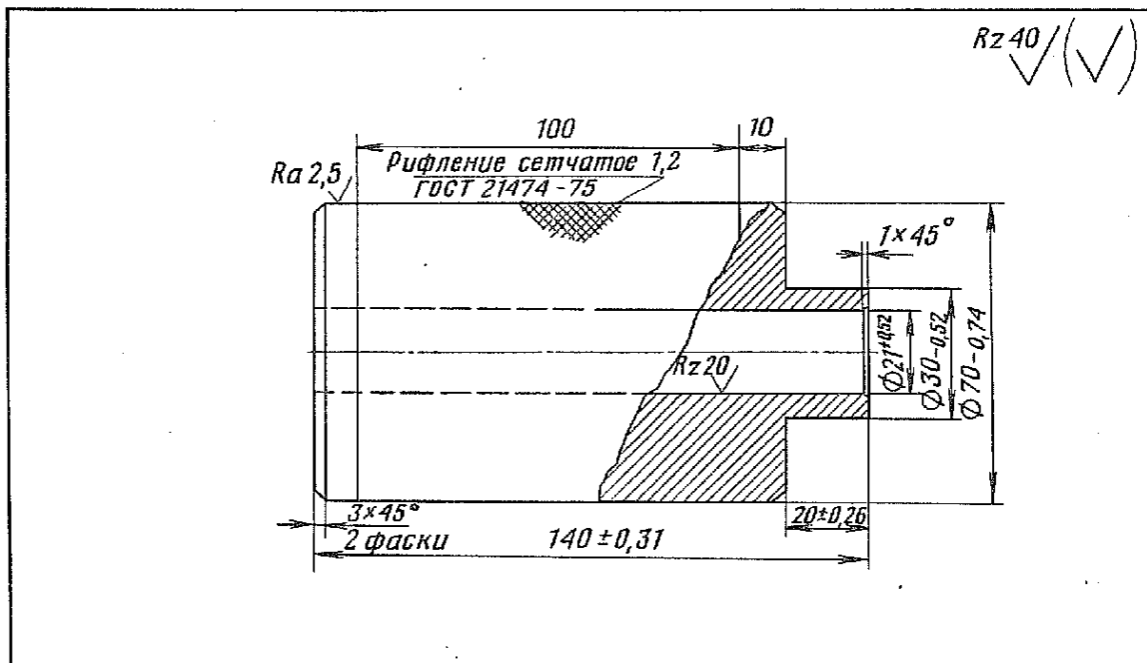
Инерционный съемник среднего подшипника приводного вала
